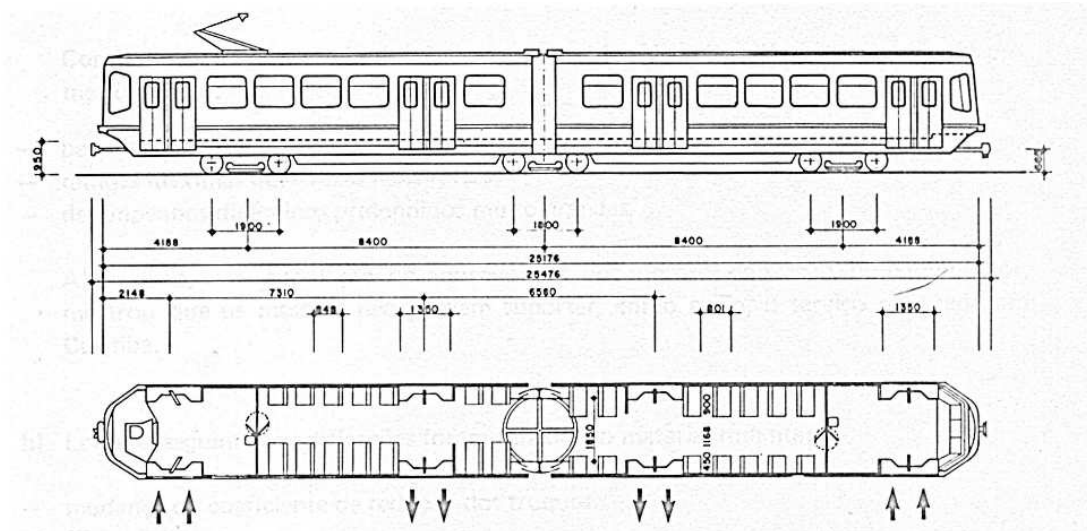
Bonde em via exclusiva - planta e elevação do bonde a ser implantado
